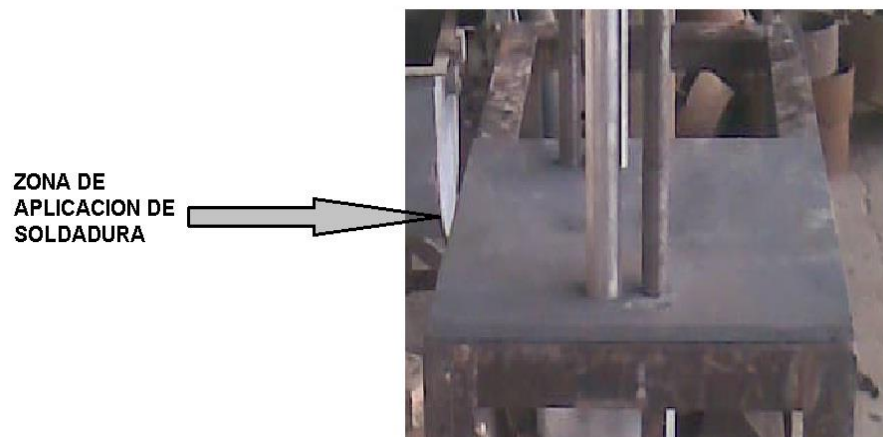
ZONA DE UNION ENTRE PLACA Y ESTRUCTURA
